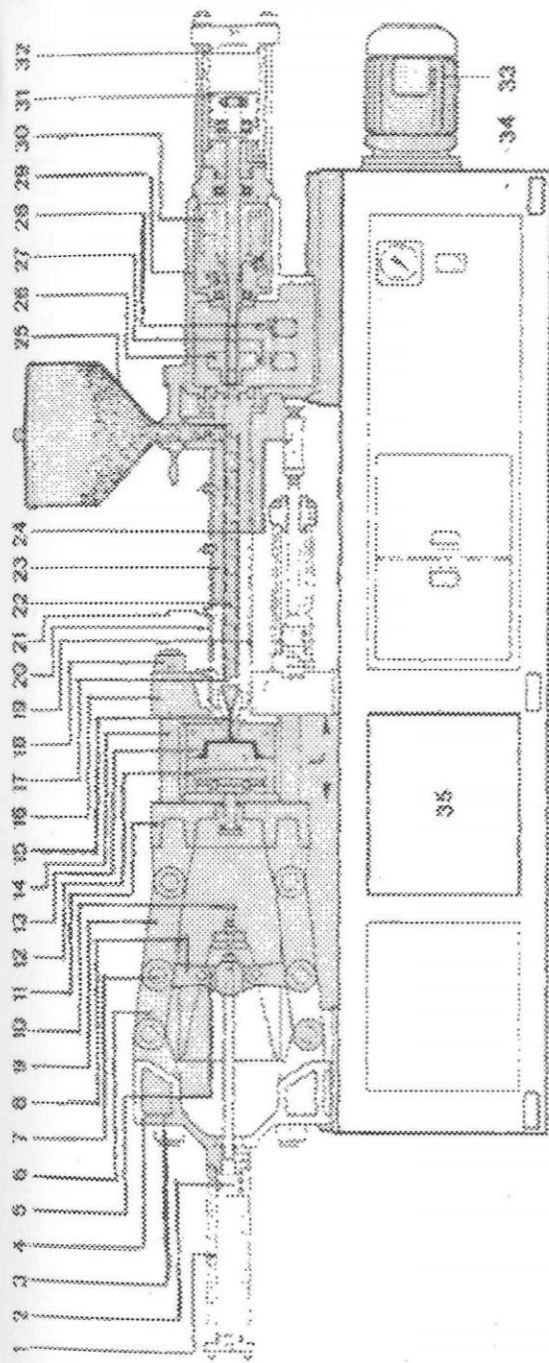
SECCIÓN LONGITUDINAL DE UNA MÁQUINA DE MOLDEO POR INYECCIÓN POR HUSILLO RECIPROCANTE, DEL TIPO DOBLE RODILLERA. Nótese el molde cerrado y el husillo (22) en posición al final de la inyección.
